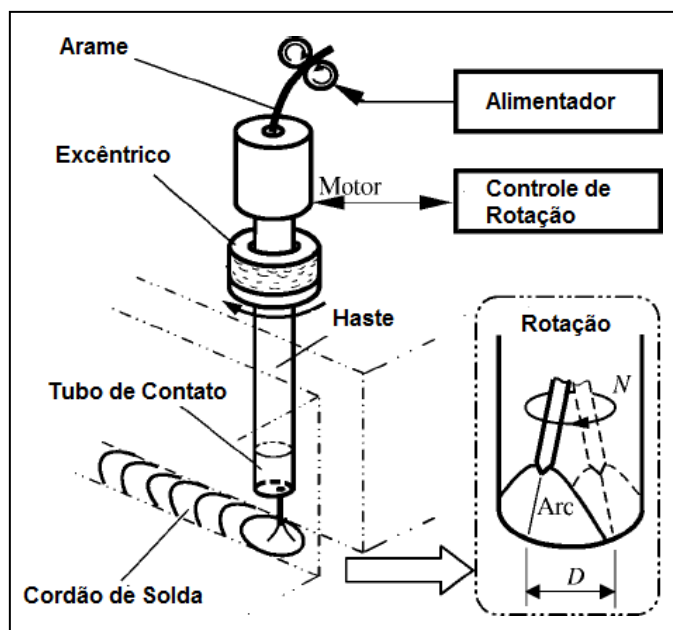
Esquema similar da tocha com eletrodo rotativo [13].
